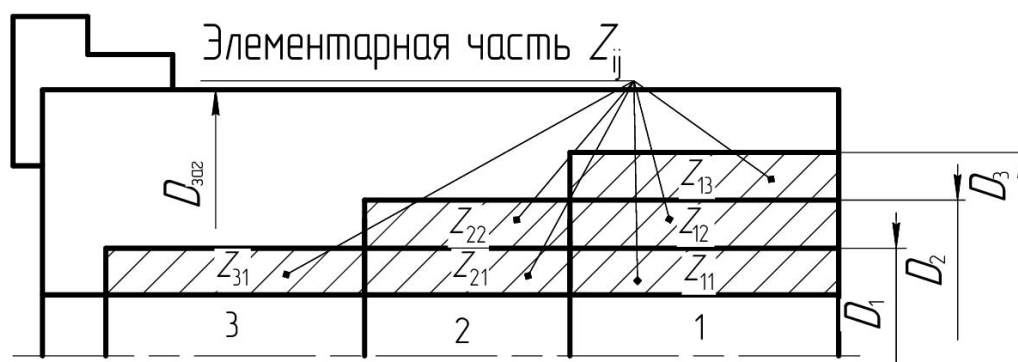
Схема разбиения общего припуска трехступенчатого отверстия на элементарные части
